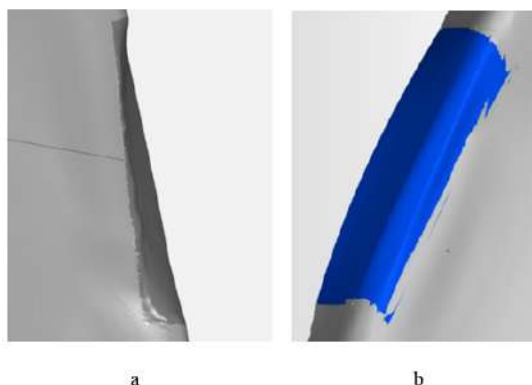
Stav povrchu pred digitálnou rekonštrukciou (Urban, 2025)
